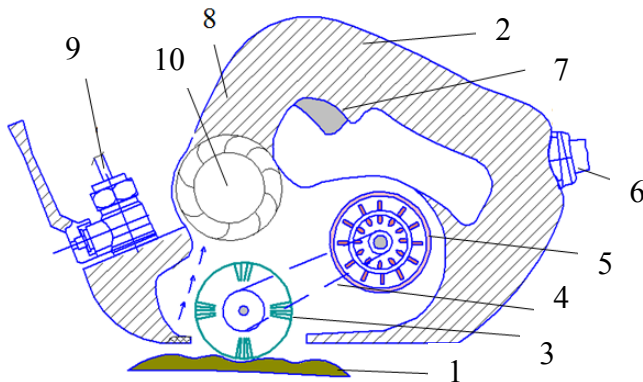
Устройство для очистки кожного покрова животных с приводом от коллекторного электродвигателя:
